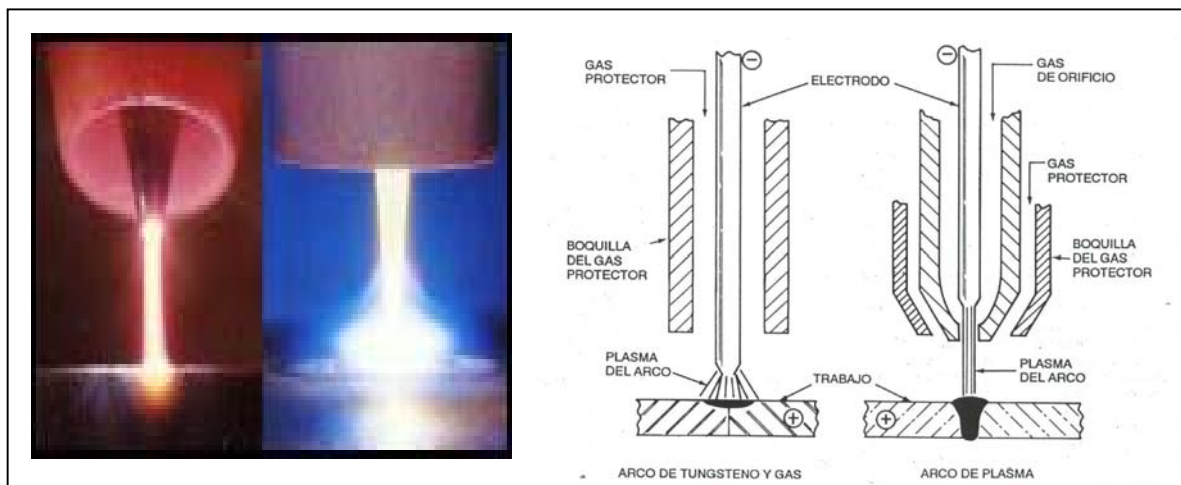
Comparación de los procesos de soldadura GTAW y PAW.
